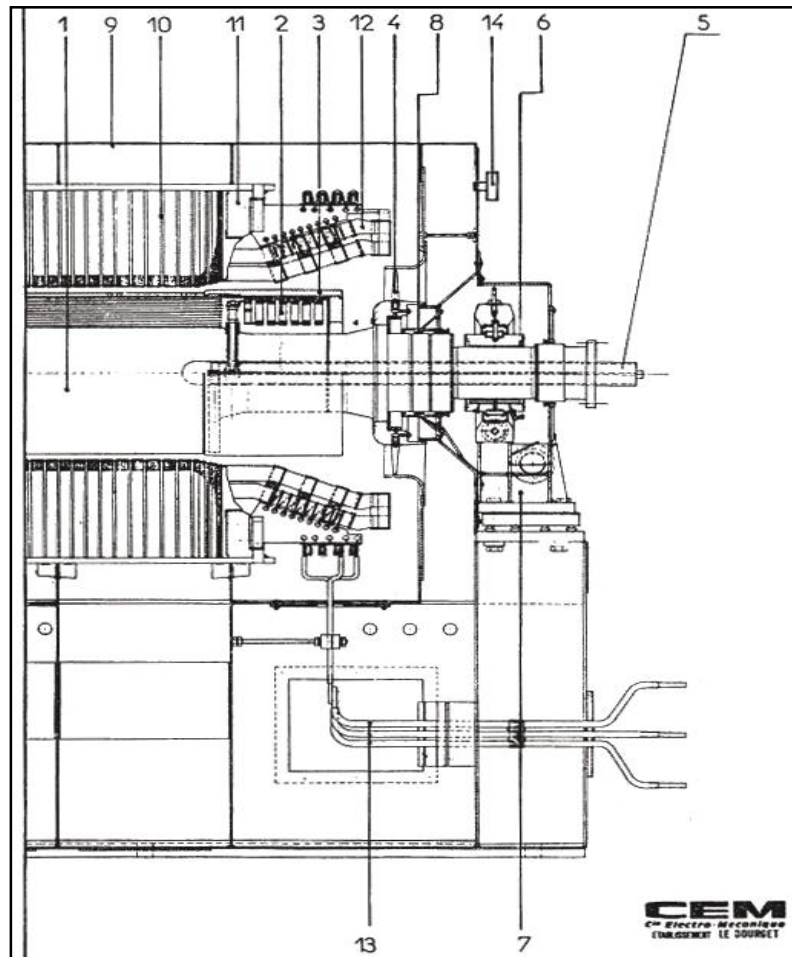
SCHEMA DE COUPE D'UN ALTERNATEUR DE LA CENTRALE
